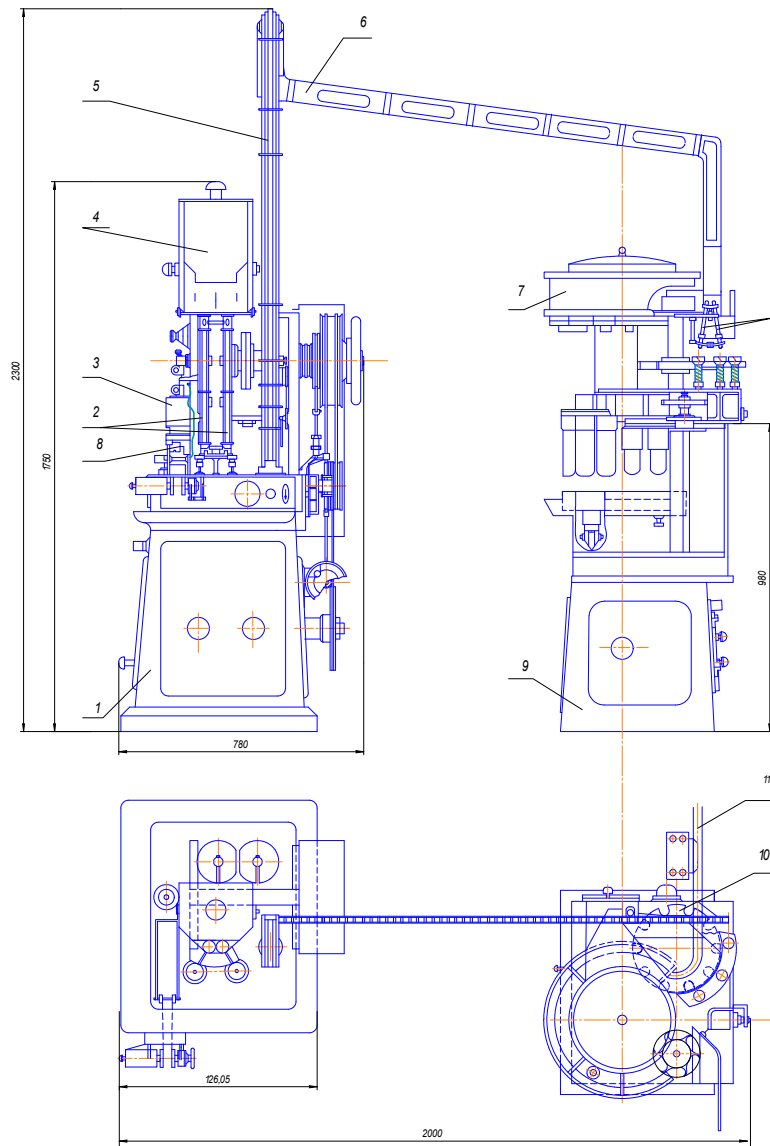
Штамповочно-укупорювальний агрегат
